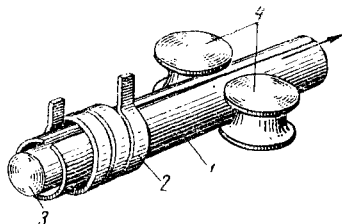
Схема радиочастотной сварки с индукционным подводом тока
